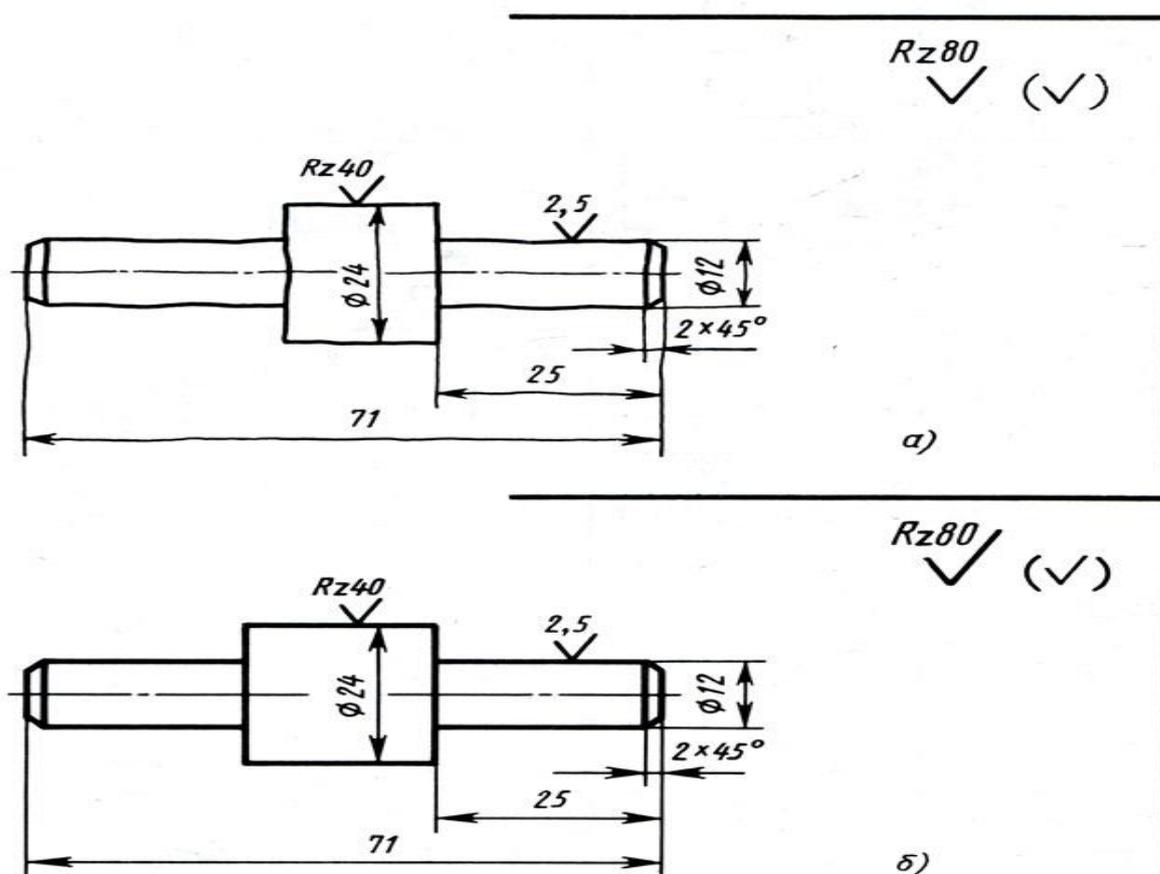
Сравнение эскизов и чертежа: а - эскиз; б - чертеж
